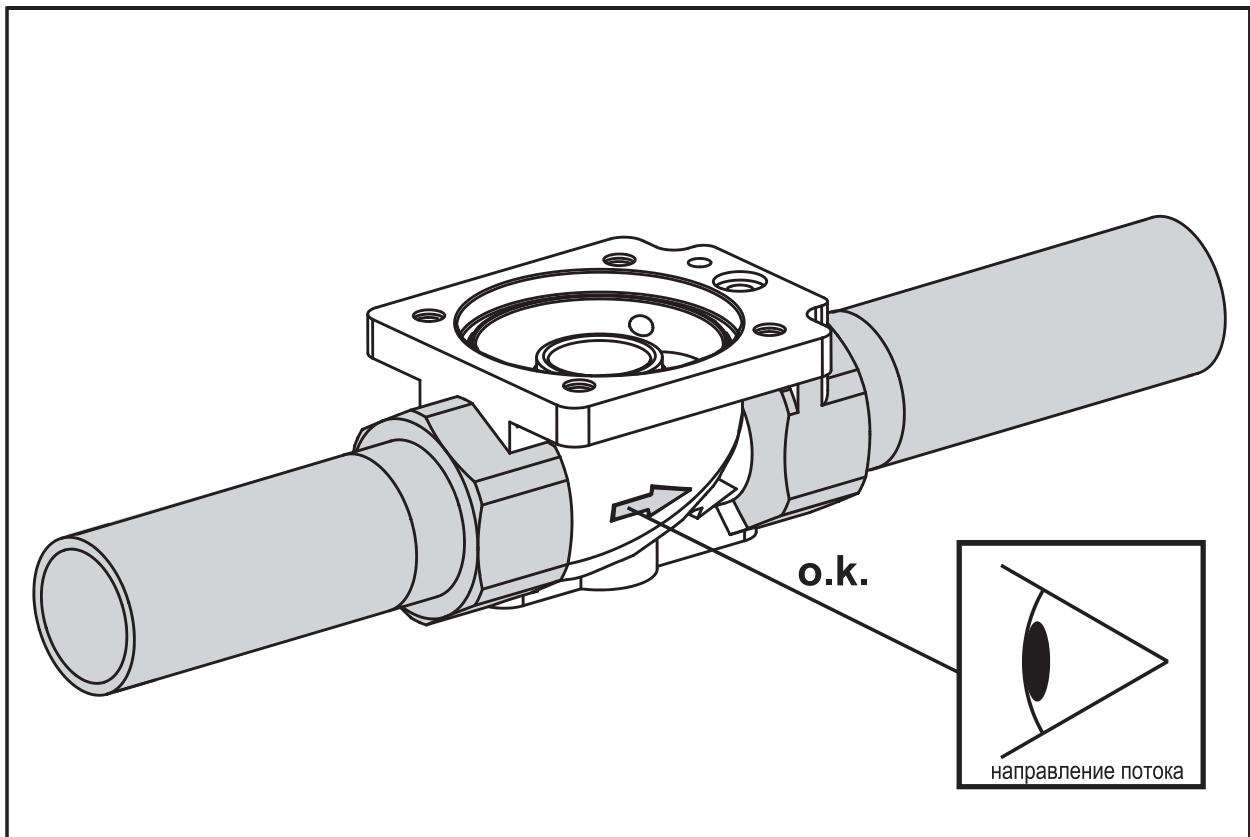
Монтаж/демонтаж – сварное соединение, приваривание корпуса
